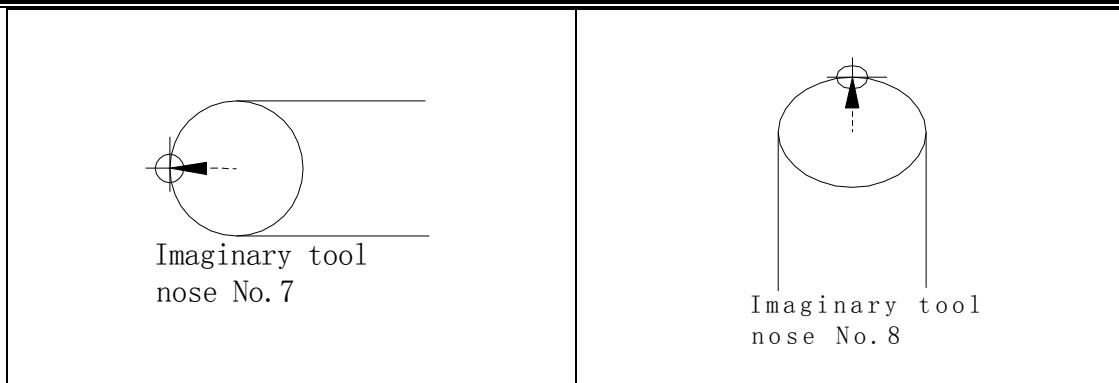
Присвоенный номер носа инструмента в передней системе координат инструмента
